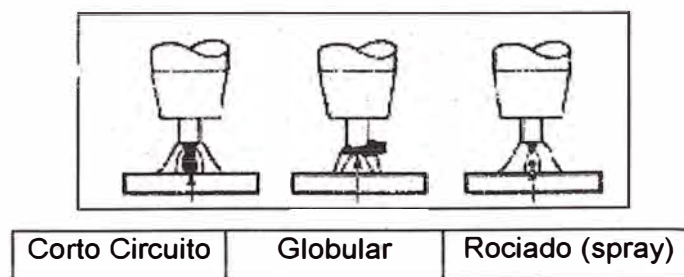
Técnicas de soldadura MIG más empleadas.
